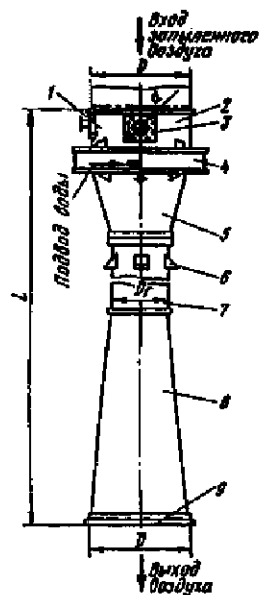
Труба Вентури: 1 – лаз герметический; 2 – цилиндр; 3 – смывное приспособление; 4 – камера; 5 – конфузор; 6 – опора; 7 – горловина; 8 – диффузор; 9 – фланец.
